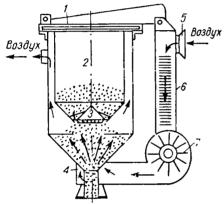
Установка для предварительного подогрева и сушки полимерного материала:
